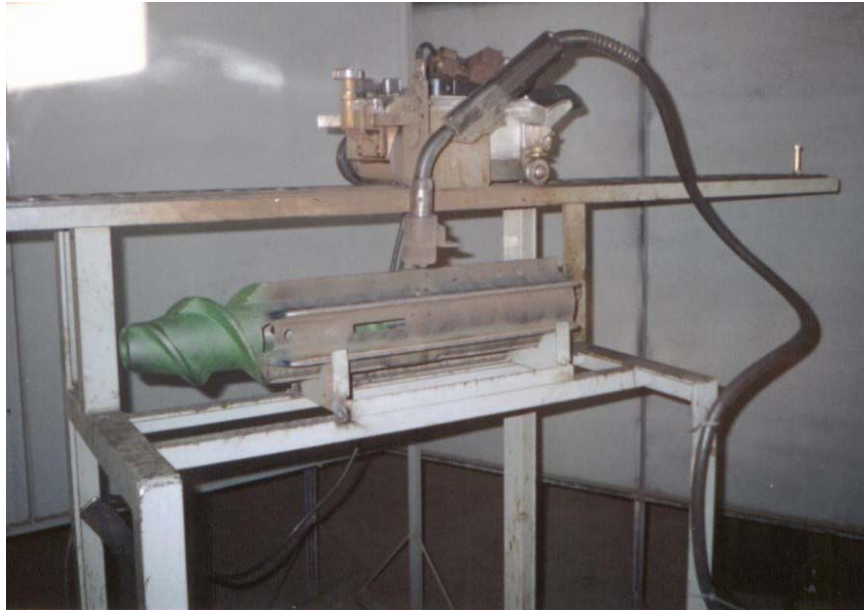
Preparação para Soldagem dos Corpos de Prova
